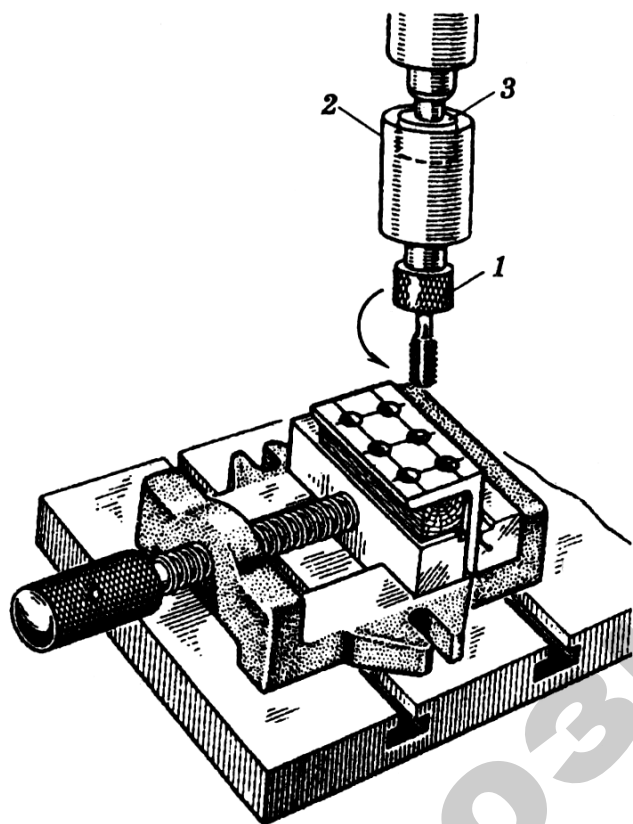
Нарезание внутренней резьбы на сверлильном станке:
